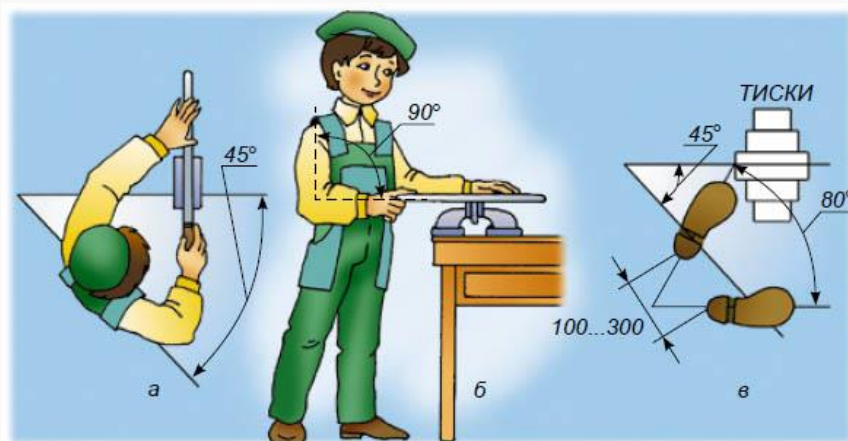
Положение при опиливании: а – туловища; б – корпуса тела человека; в – ступней ног
